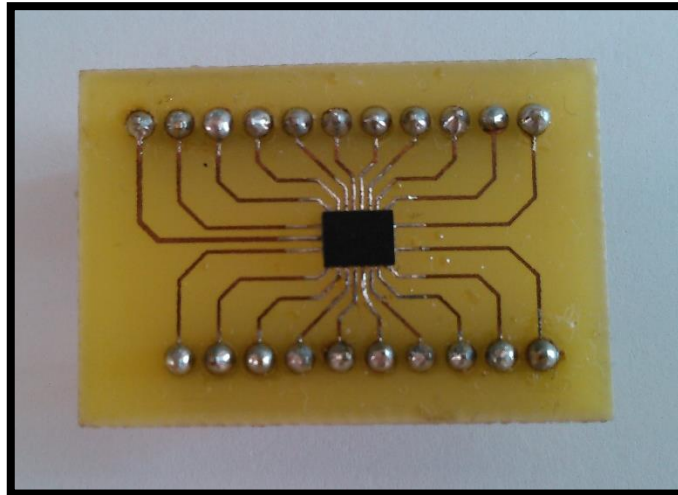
PCB del zócalo para el chip bq51050B (vista superior)
